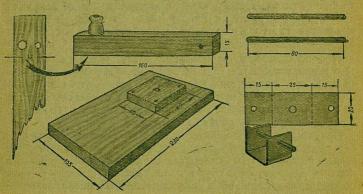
Детали перфоратора: доска основания, рычаг, шпильки и подшипник.
